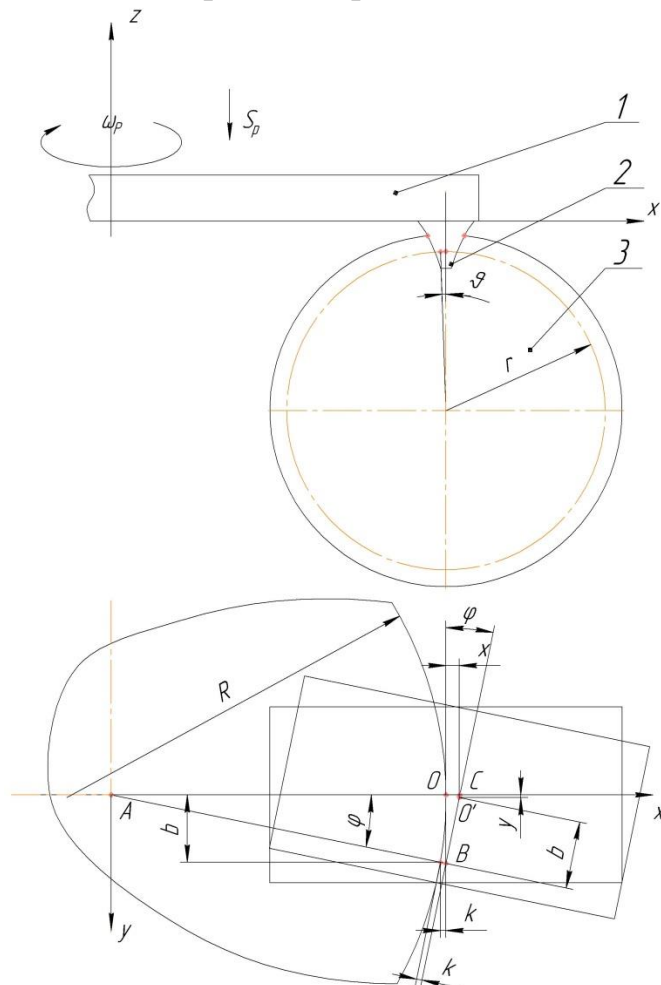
Схема формоутворення методом копіювання зі зміщенням заготовки
